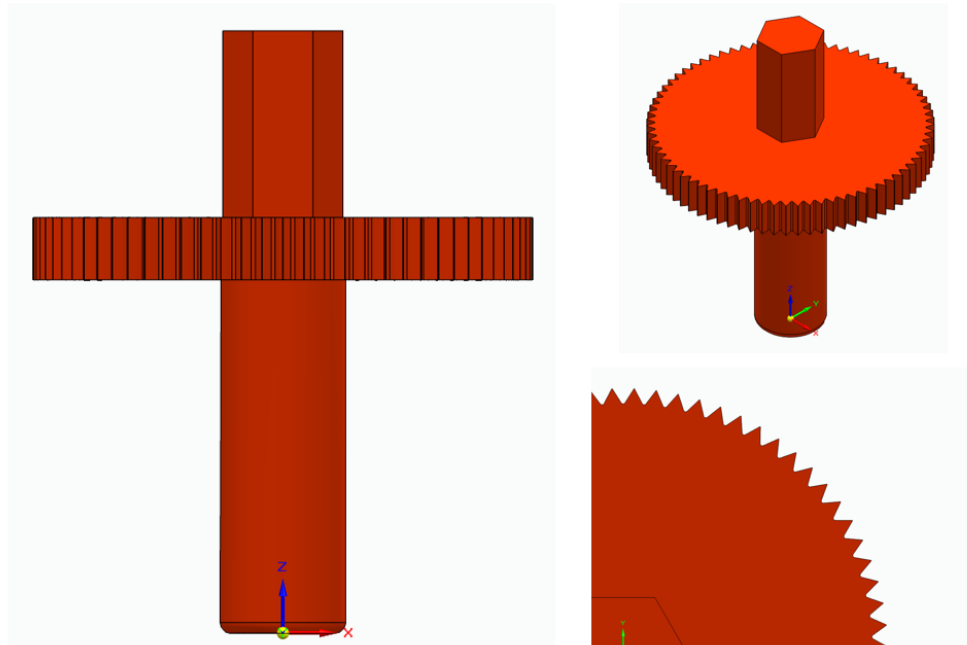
Engranaje reductor con eje hexagonal, realizado con Solid Edge
